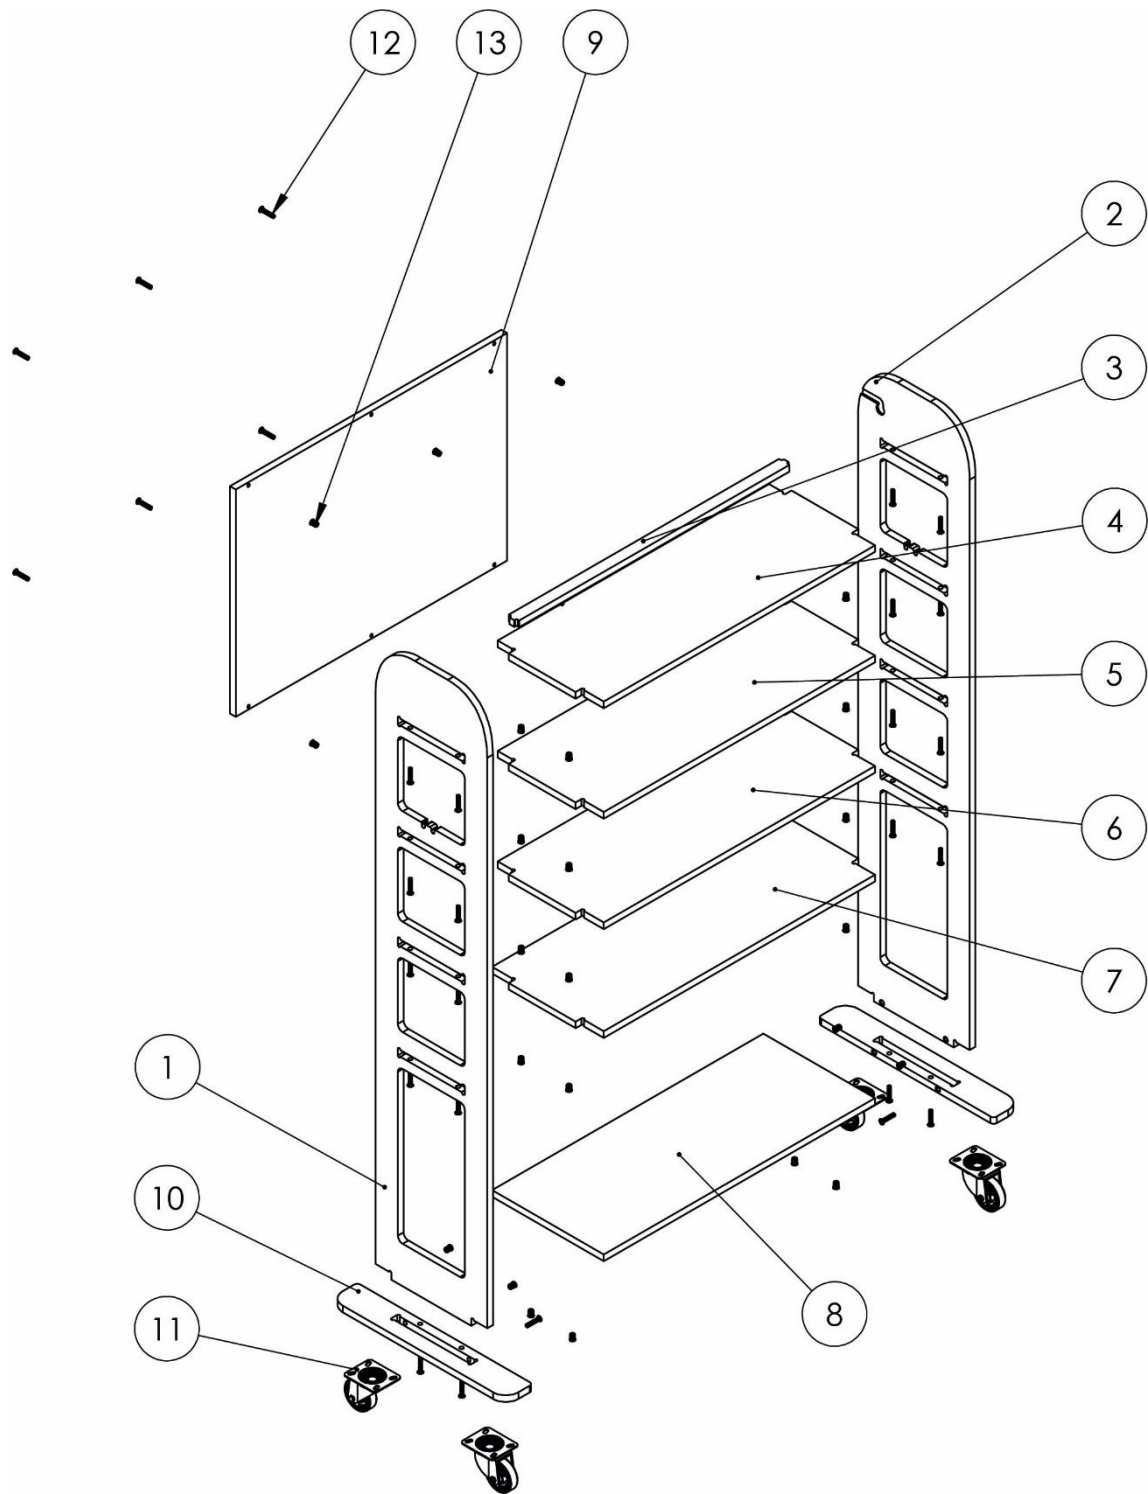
Fuente propia. Explosionado de las piezas de la estantería.
